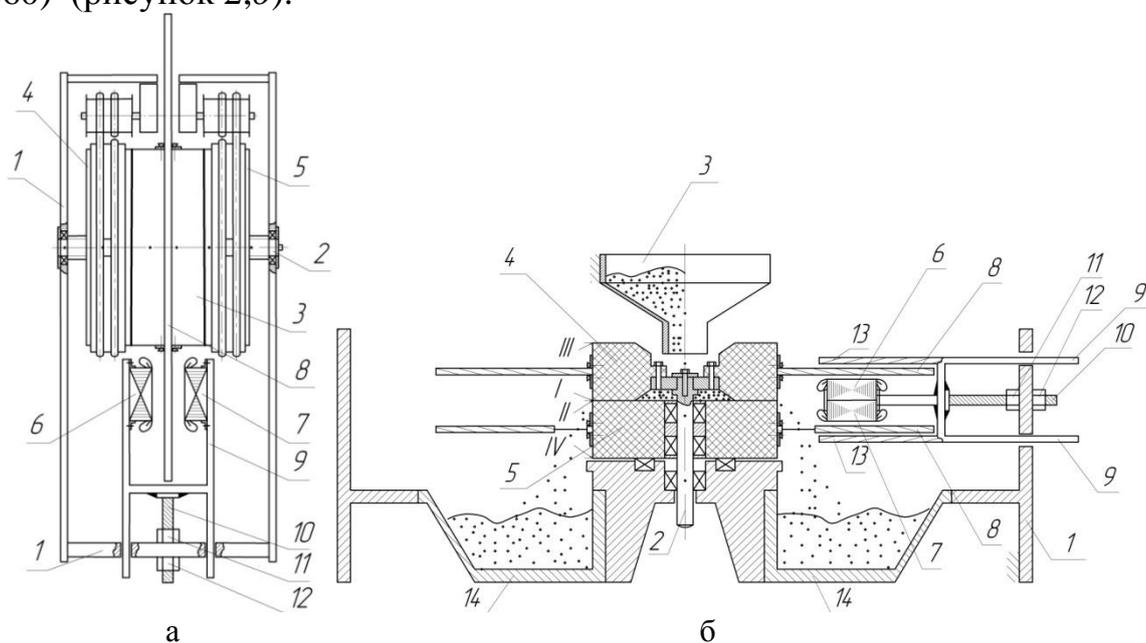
Варианты компоновки ЖМ с ЛЭП (схематично): *а* – с одним вращающимся жерновом: 1 – корпус; 2 – ось; 3 – вращающийся жернов; 4,5 – неподвижные жернова; 6,7 – индукторы плоского двухстороннего ЛАД; 8 – вторичный элемент ЛАД (алюминиевый диск); 9 – рама; 10 – регулировочный винт; 11,12 – фиксирующие гайки; *б* - с двумя вращающимися в противоположные стороны верхним и нижним жерновами: 3 – загрузочный бункер; 4,5 – верхний и нижний жернова; 13 – ферромагнитные элементы ЛАД; 14 – приемные емкости; I,II,III,IV – мелющие поверхности жерновов.
